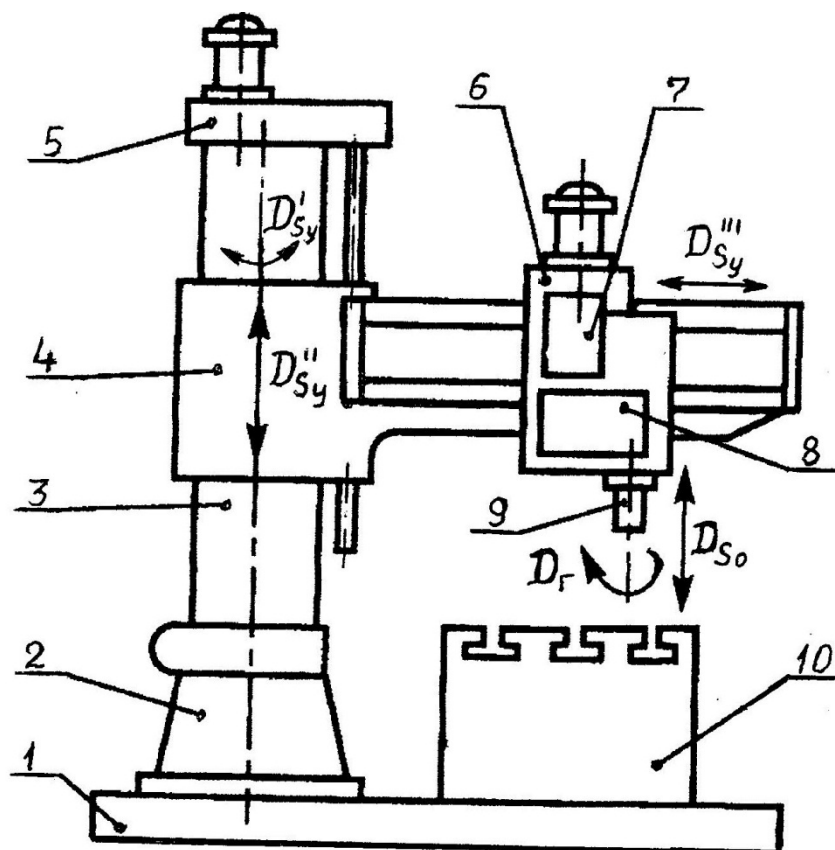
Общий вид радиально-сверлильного станка: 1 - фундаментная плита; 2 – колонна; 3 – поворотная гильза; 4 – траверса (рукав) с направляющими для перемещения сверлильной головки; 5 – механизм фиксированного перемещения траверсы по высоте; 6 – сверлильная (шпиндельная) головка; 7 – коробка скоростей; 8 – коробка подач; 9 – шпиндель; 10 – стол;  $D_r$  – главное движение (вращение шпинделя с инструментом);  $D_{So}$  – движение осевой (вертикальной) подачи;  $D_{Sy}'$  – установочное фиксированное движение поворота гильзы с траверсой;  $D_{Sy}''$  – установочное фиксированное движение траверсы по гильзе;  $D_{Sy}'''$  – установочное фиксированное движение сверлильной головки по направляющим траверсы
